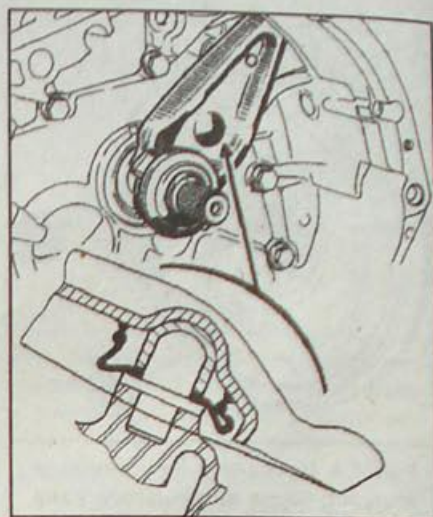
Расположение чехла для опоры вилки выключения сцепления, заполненного смазкой (коробка передач JC)
